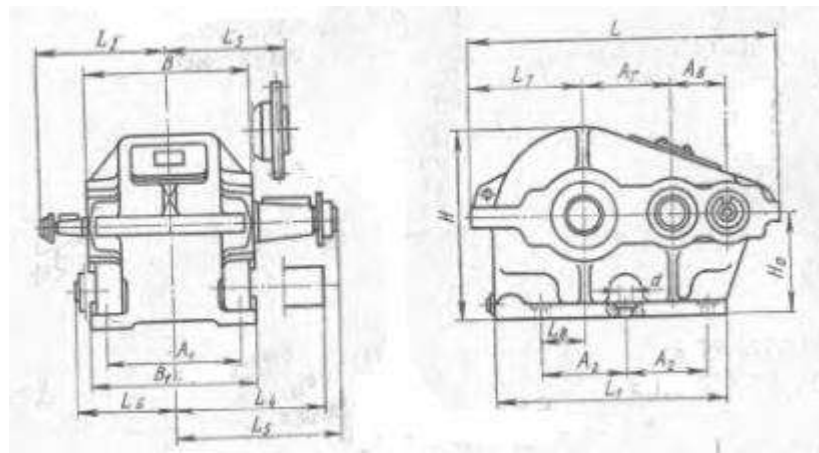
Ескіз редуктора Ц2У-400-К-31,5-22М1
